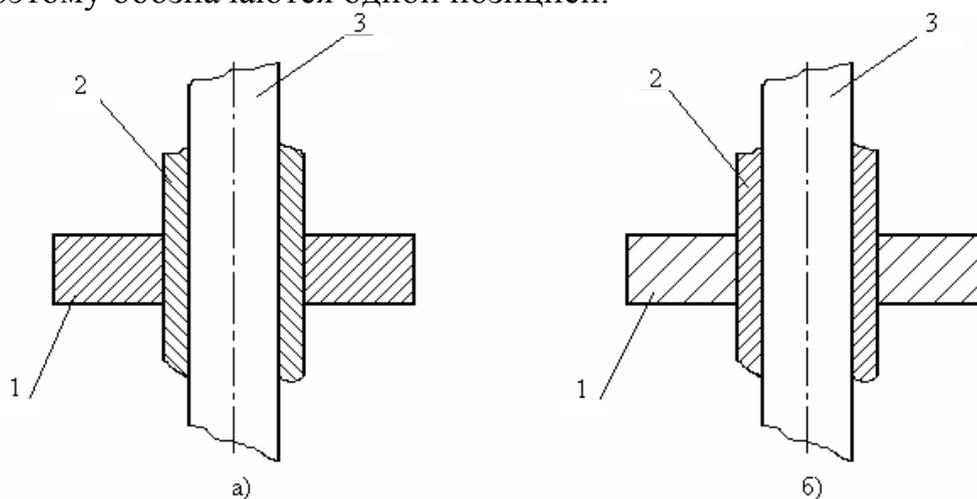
Нанесение штриховки на сборочных чертежах
